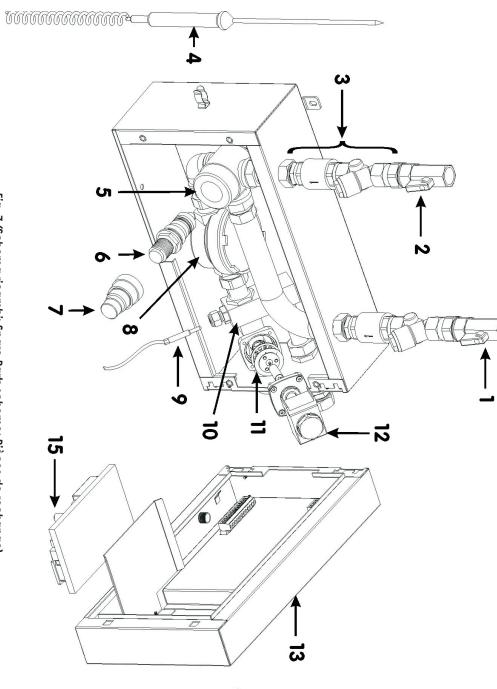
(Schema ricambi; Spare Parts scheme; Pièces de rechange)
